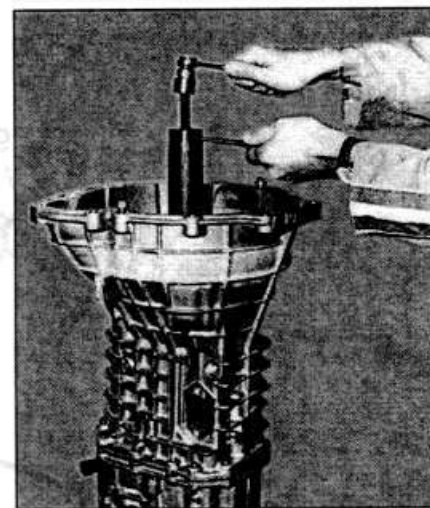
Снятие задней крышки с картера коробки передач приспособлением 16.041
